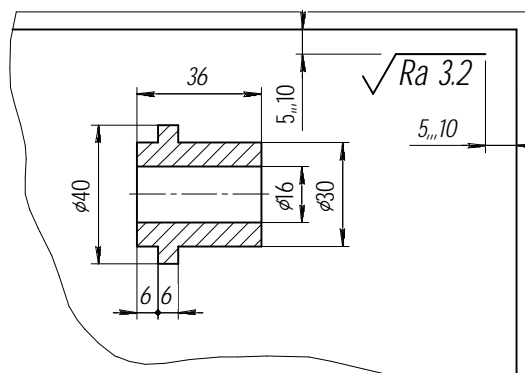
Чертеж детали с одинаковой шероховатостью поверхностей
